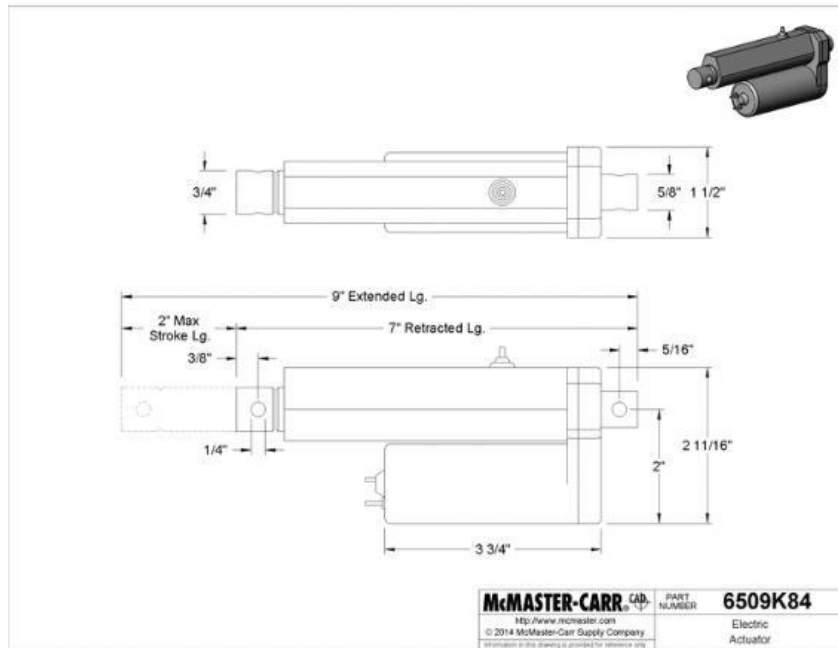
Medidas del actuador que va a mover el molde y el pistón neumático
